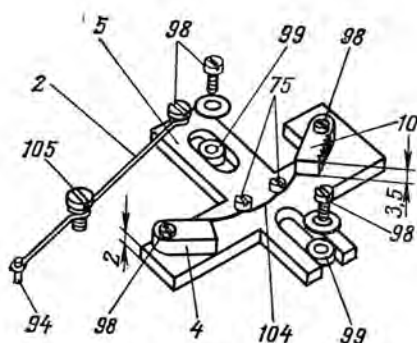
Тормозное устройство: 2 — рычаг тормоза, проволока стальная класса II диаметром 0,8 мм; 4 — колодка тормоза подающего узла, резина; 5 — планка тормоза, Д16А-Т; 10 — колодка тормоза приемного узла, Л62-Т; 75 — винты М2×3, 2 шт.; 98 — винт М2×5, 5 шт.; 99 — втулка, ЛС59-1, 2 шт.; 104 — пружина, проволока стальная класса II диаметром 0,5 мм; 105 — винт М3×10.
